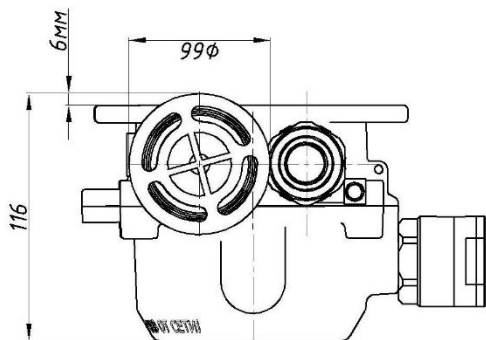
Монтаж ОСЗВ к газоанализатору ИДК-10, внешний вид и габаритные размеры
